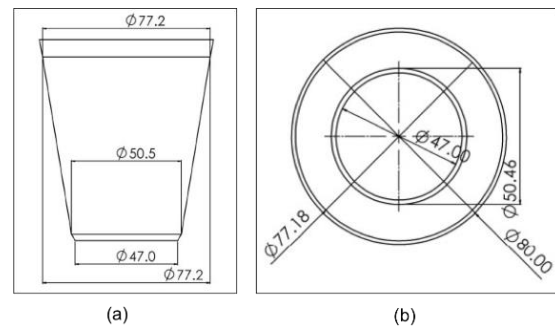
Dimensiones principales de la pieza, a) vista lateral y b) base superior e inferior.
